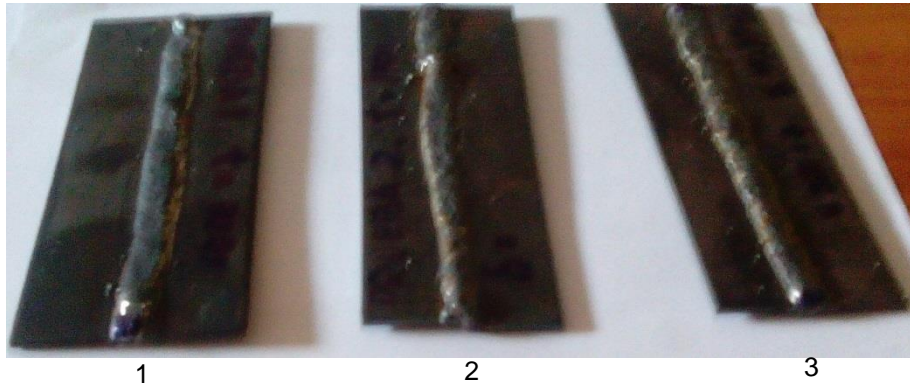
Juntas soldadas con placas de 25.4 mm de ancho.
